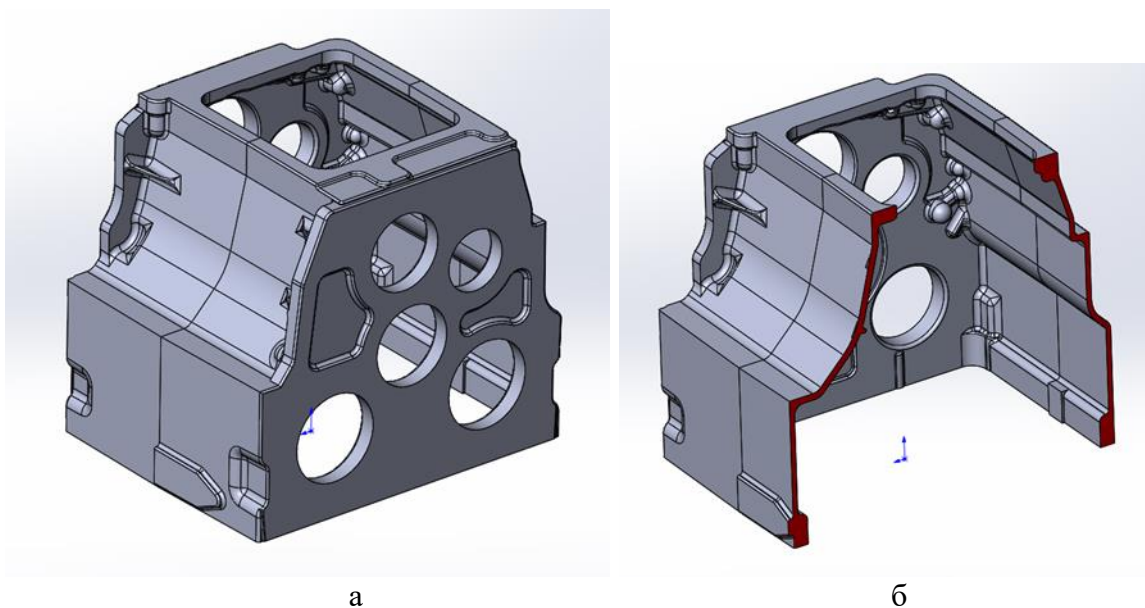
а – Виливок корпусу гідромеханічної трансмісії; б – поперечний розріз виливка
